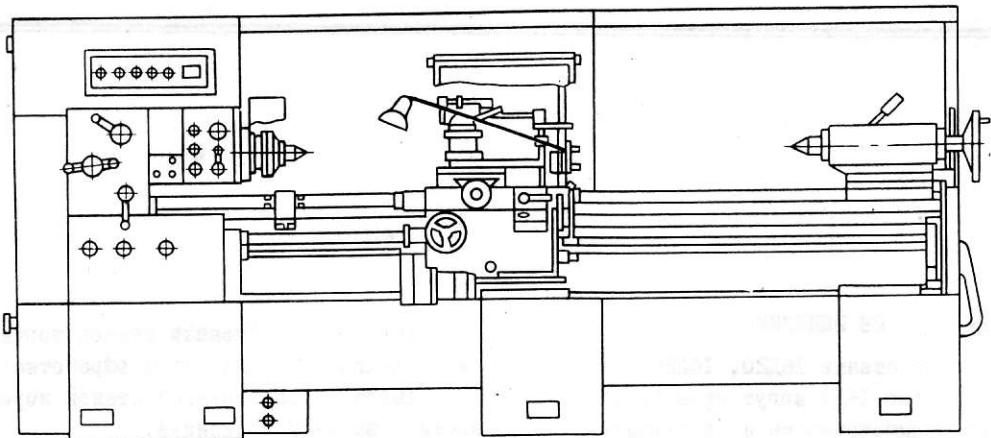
Станок токарно-винторезный И6Д25 с длиной обработки L = 2000 мм
